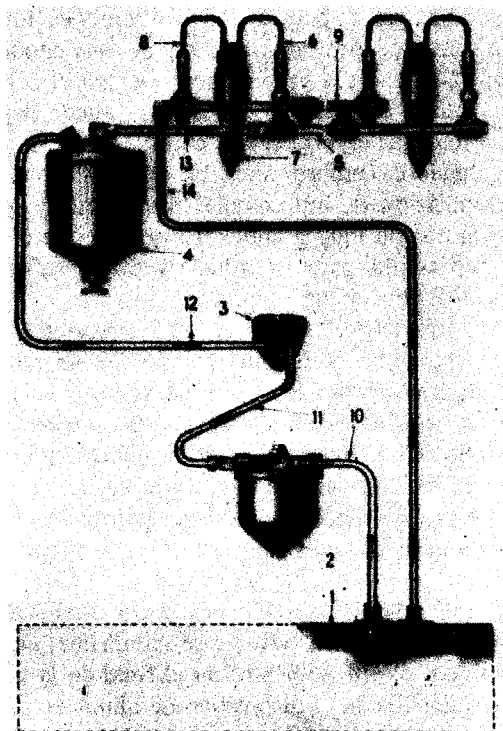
Sistema de alimentación de gasoil en un motor Diesel (Detroit Diesel Engine Division of General Motors Corporation).
